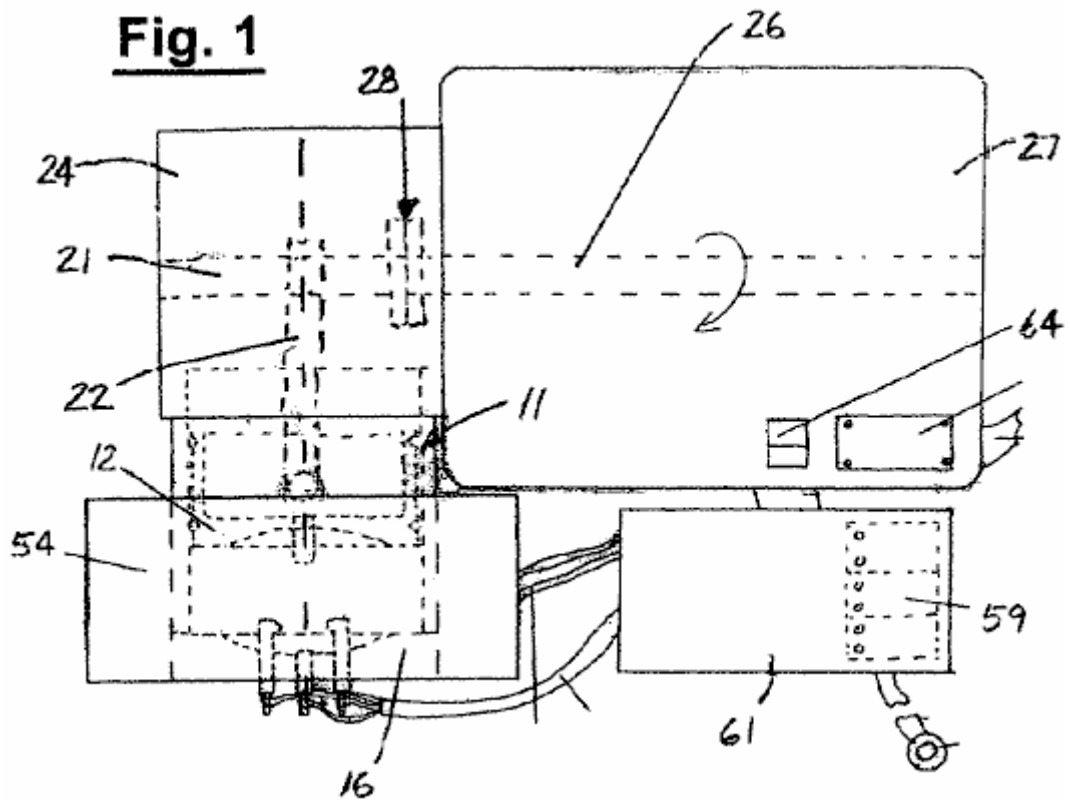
ist eine Draufsicht auf eine Ausführungsform eines internen Explosionsmotors und Generators gemäß der Erfindung.
